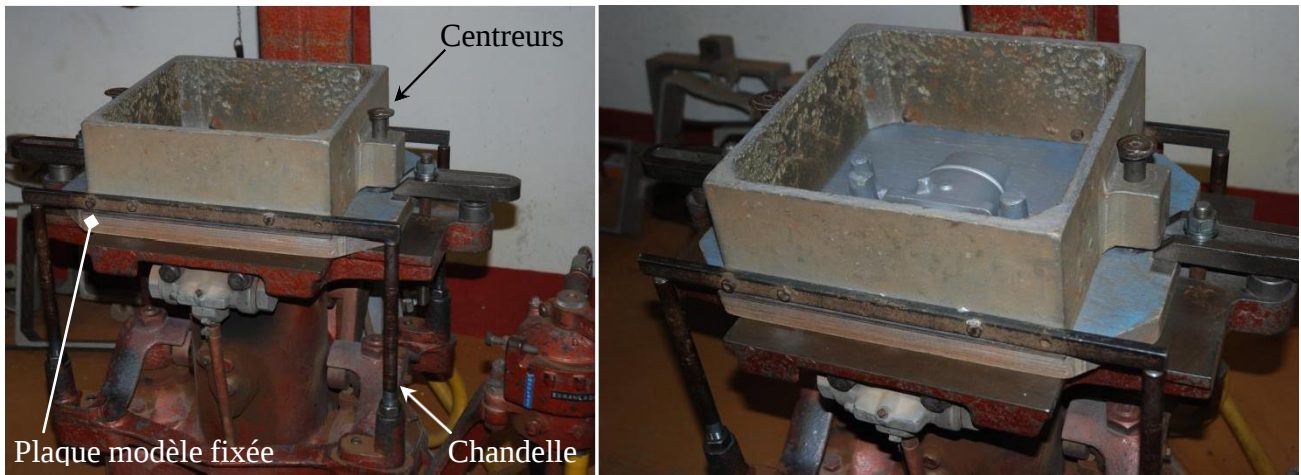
Plaque modèle fixée sur la machine et le châssis positionné
